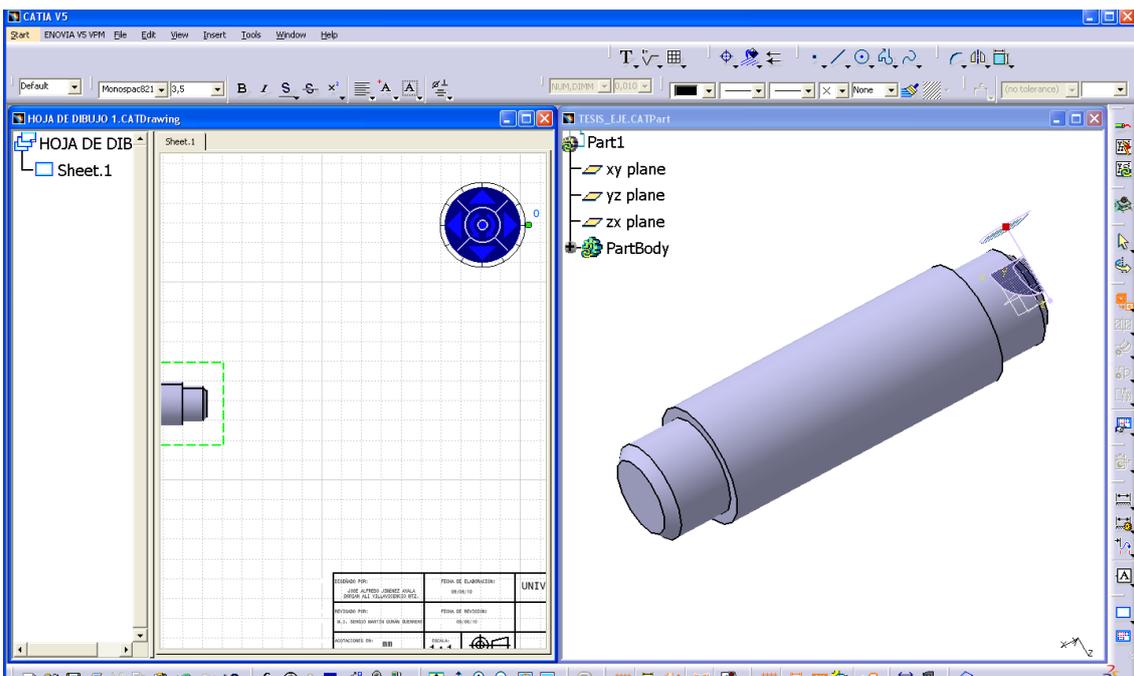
Desplazamiento de la vista frontal hacia la izquierda.
